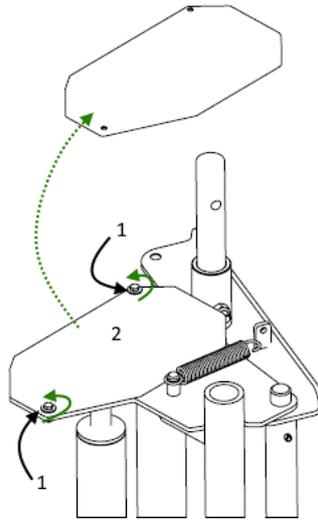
Desmontaje de la cubierta de la transmisión del dispensador
